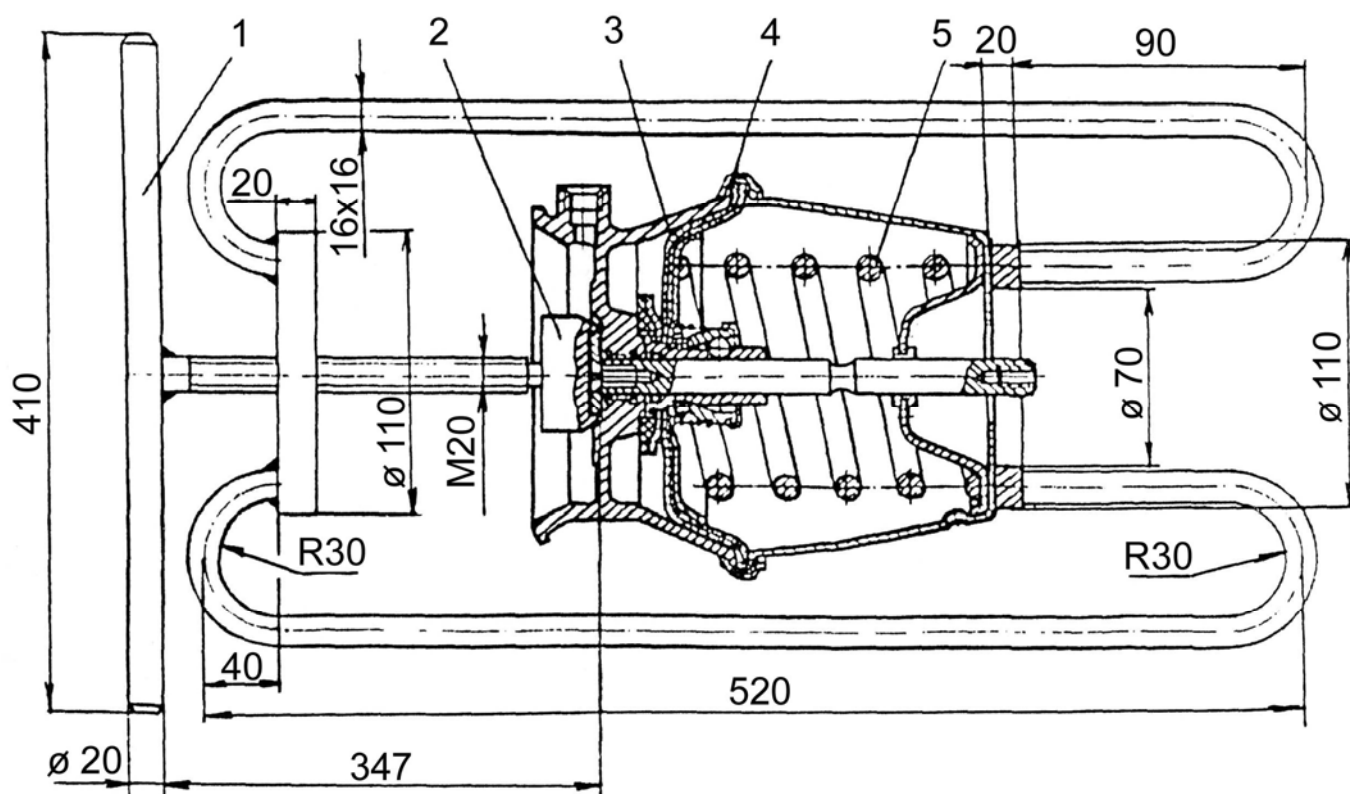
Приспособление для разборки пружинного энергоаккумулятора:
